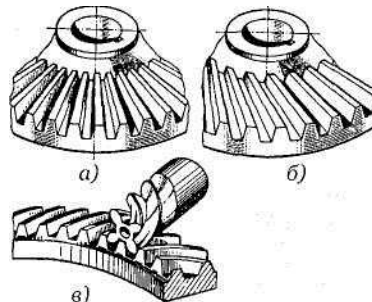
Конические зубчатые колеса: а — колесо с прямыми зубьями; б — колесо с косыми зубьями; в — колесо с круговыми зубьями
